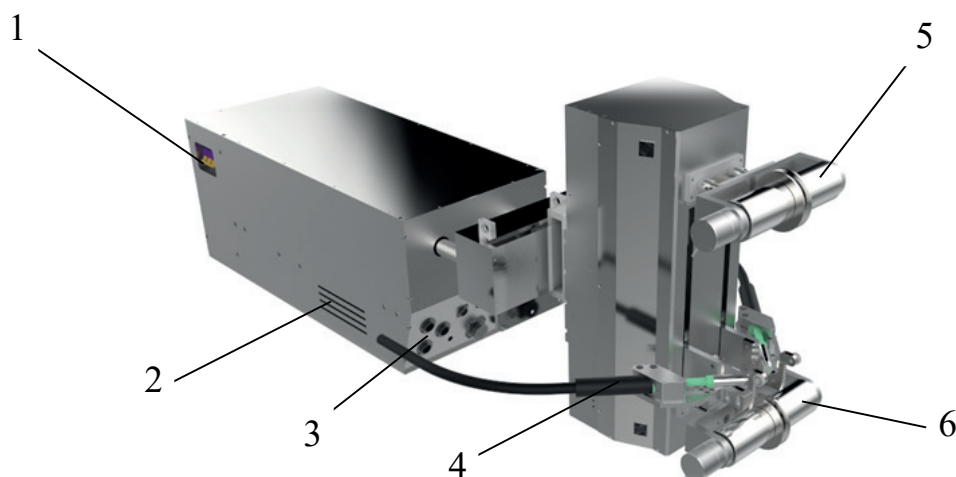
б – Схема устройства автоматического сварочного робота: 1 – выключатель питания, 2 – отверстия для охлаждения, 3 – порт для кабеля управления, 4 – сварочная горелка, 5 – верхний ролик поперечной арматуры, 6 – нижний ролик поперечной арматуры
